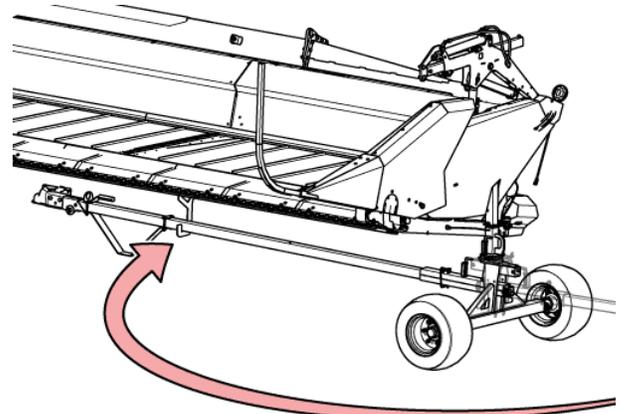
Поворот сцепного стержня в положение для хранения.
